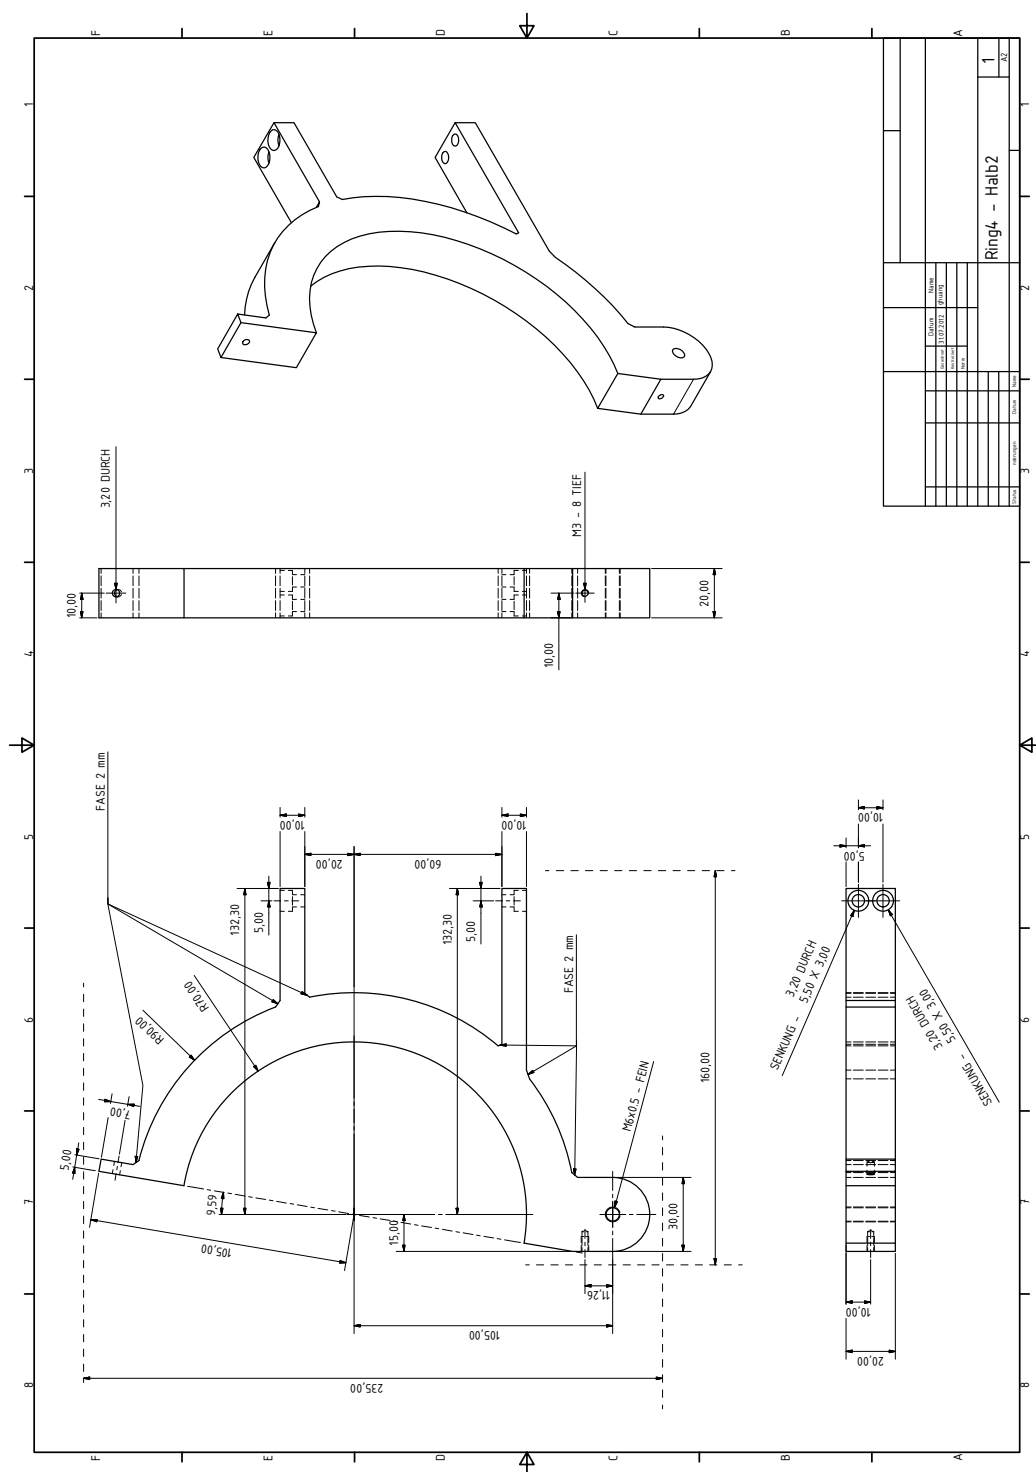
Technische Zeichnung eines Bauteils - Hälfte des oberen Rings-2
